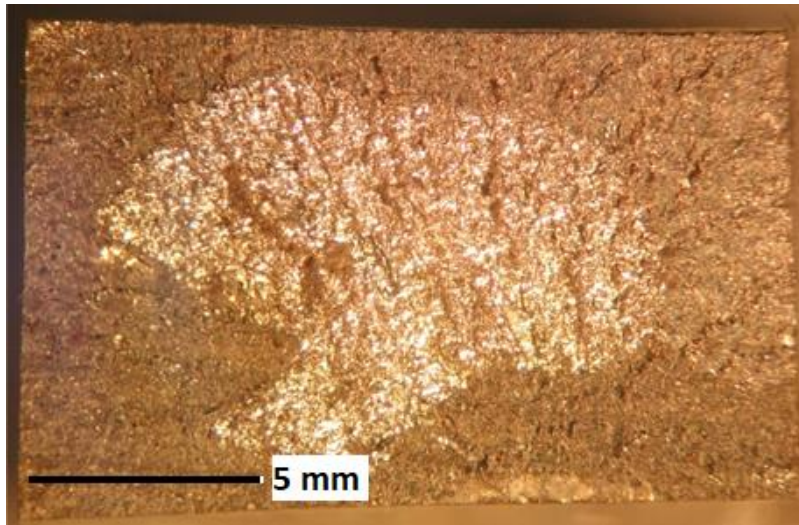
Fractura de la pieza sin precalentamiento en el ensayo de tensión.
